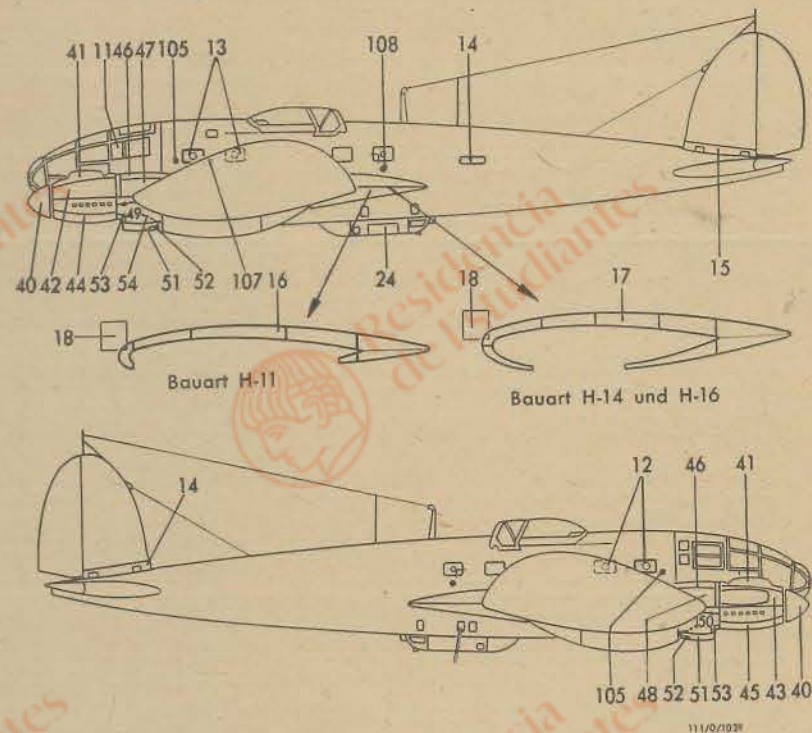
Deckel- und Klappenplan (Seitenansicht)
